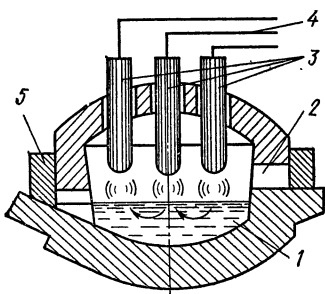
Схема трехфазной дуговой электропечи для плавки стали:
